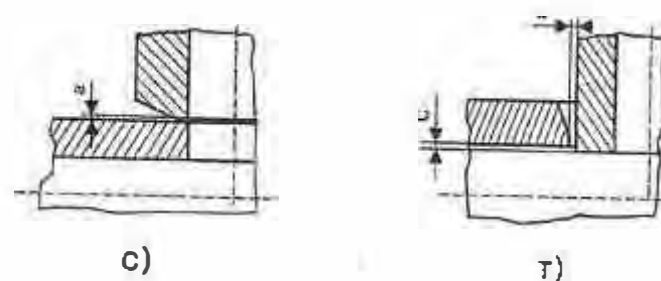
лист 3. Размеры, контролируемые измерением при сборке соединения под сварку с), т) тройниковое (угловое) соединение;
